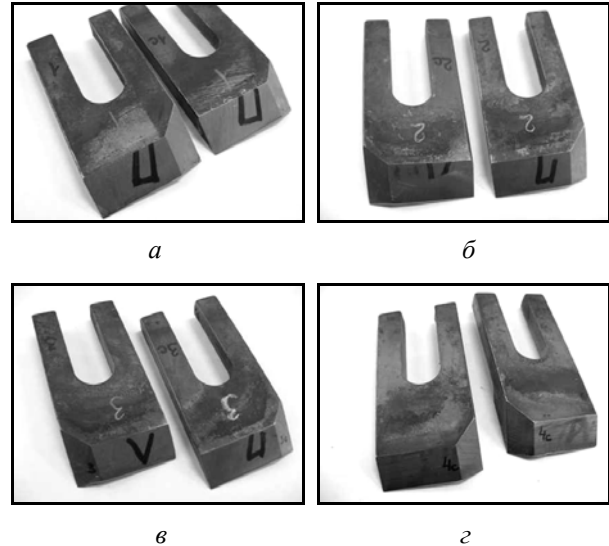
Опытные двухлезвийные ножи станка PSP 500, упрочненные различными режимами нанесения износостойких покрытий:
